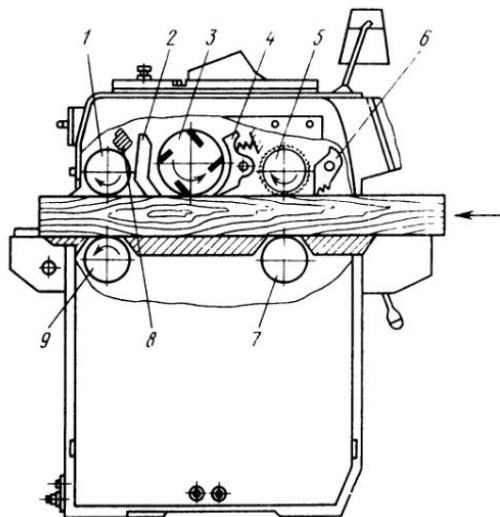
Односторонний рейсмусовый станок СР6-9:
